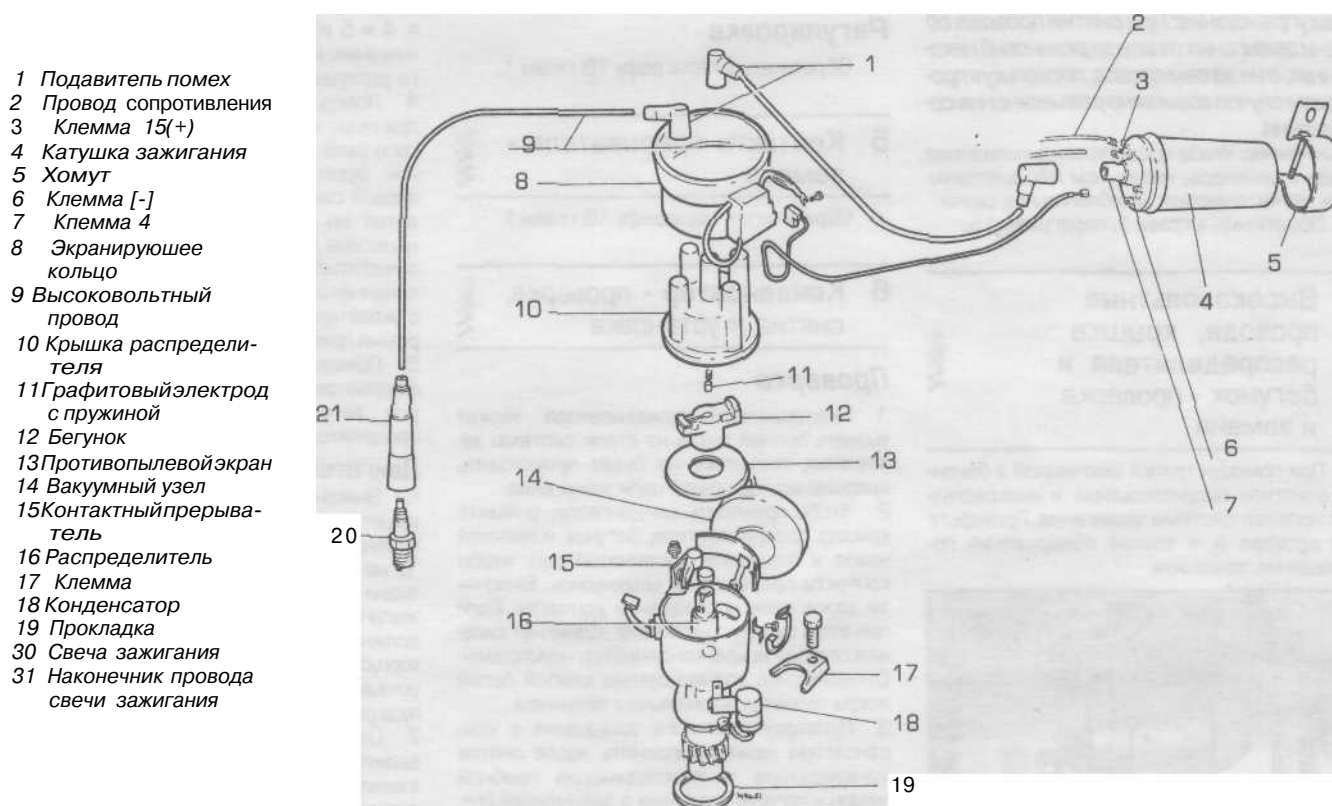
, в. Детали системы зажигания с контактным прерывателем - двигатель объемом 1,6 литра
